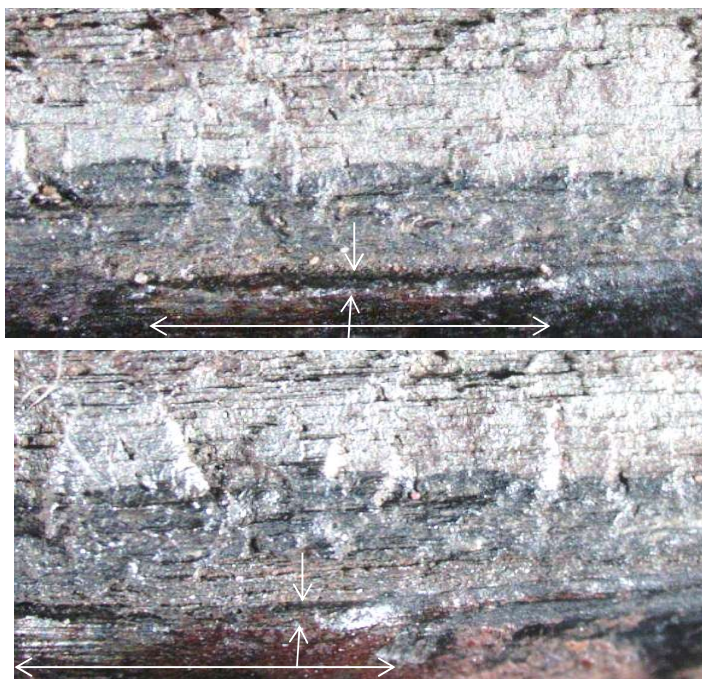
(a, b): Socavaduras en talón de soldadura en la superficie externa.
